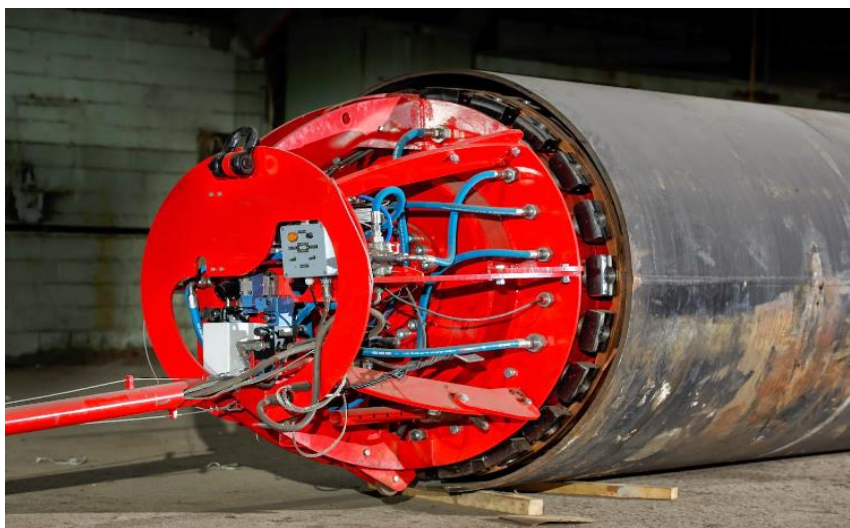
Установка внутреннего гидравлического центратора ЦВ-124 в трубе
